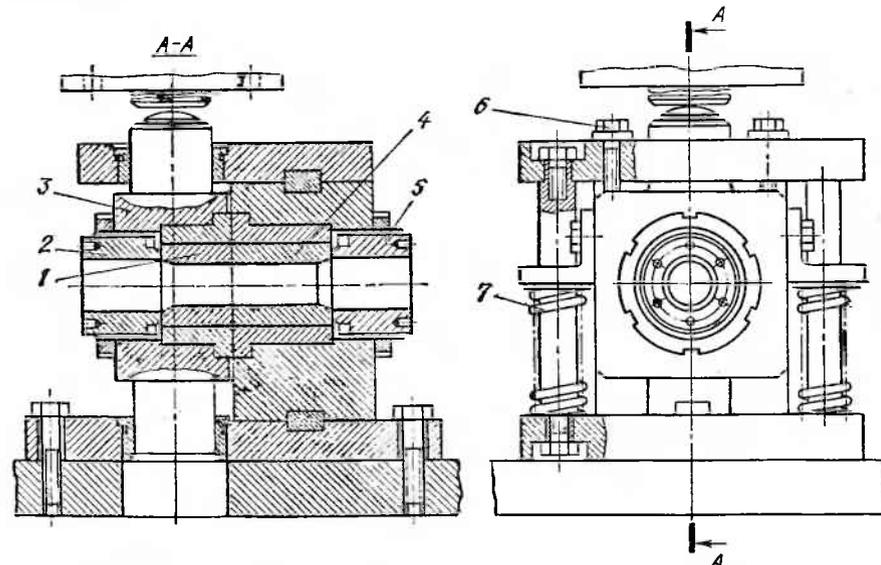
Штамп глазкового типа для резки калиброванного проката:
